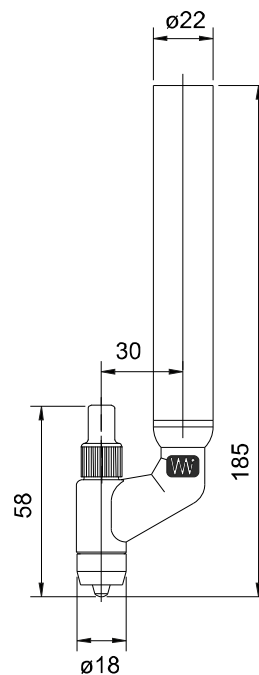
PWM 100 горелка для машинной сварки
